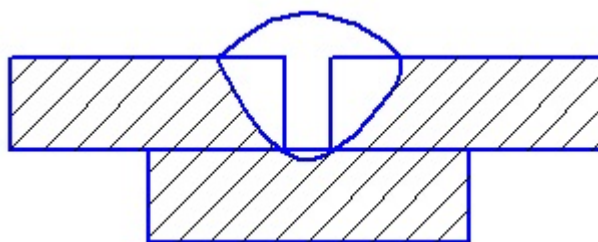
Сварное соединение С5 ГОСТ 14771-76
